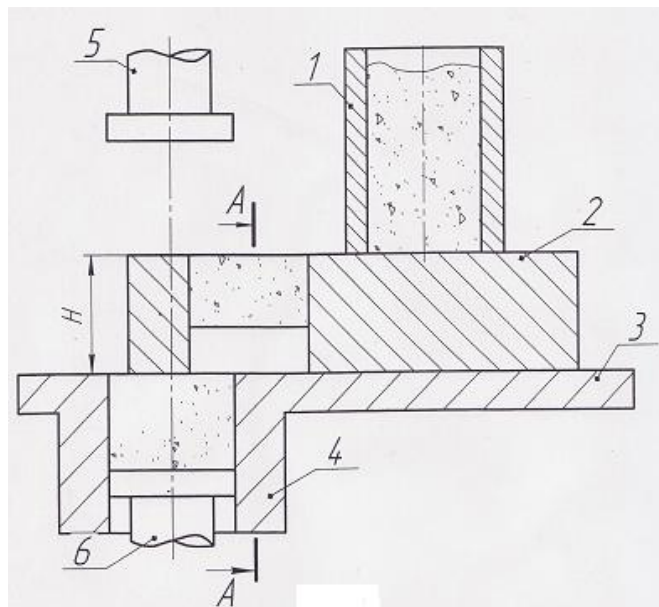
Устройство для прессования изделий с рельефной поверхностью из порошков, общий вид
